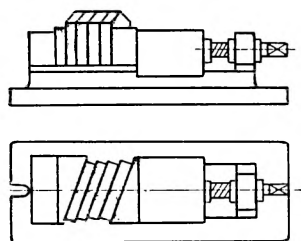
Фрезерование режущей части пластинчатых сверл в тисках с наклонными губками
